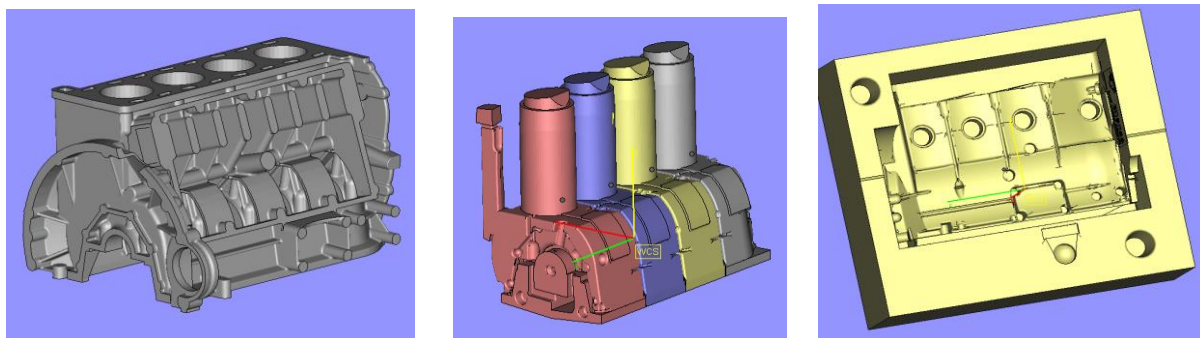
CAD-модели блока цилиндров и фрагментов песчаной формы
